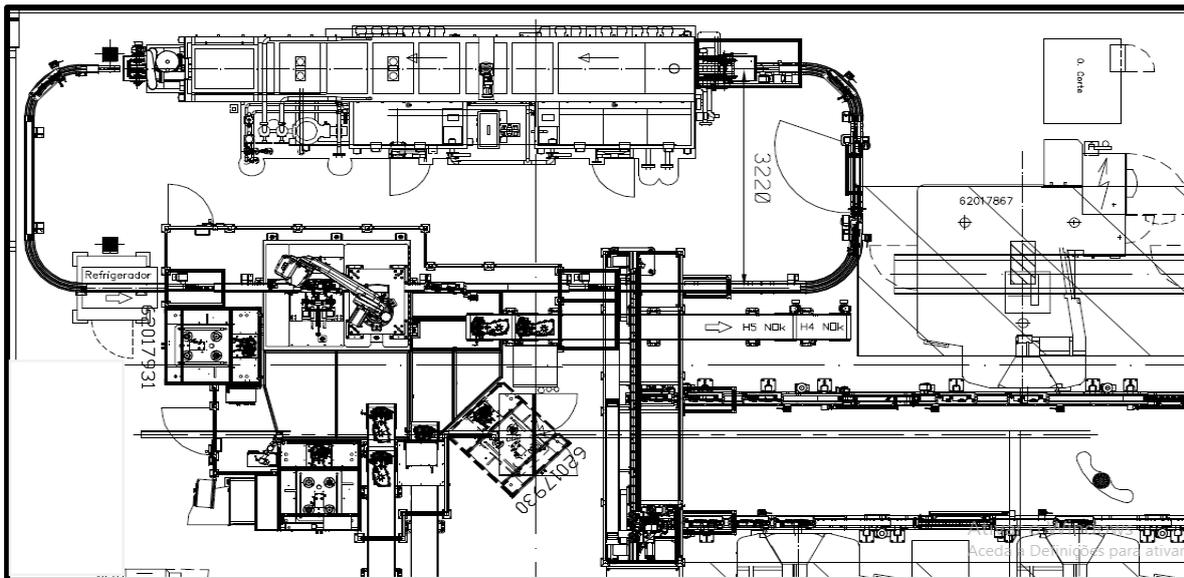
Implantação atual com pórtico de transporte entre a zona de maquinação e a zona de lavagem
